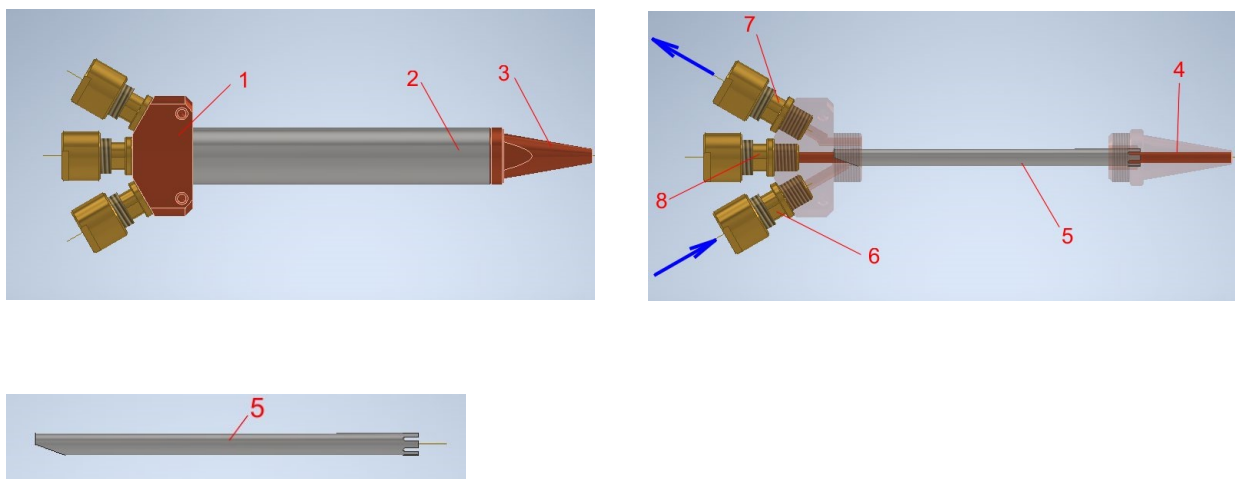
3D модель одноканального сопла для подачі газопорошкового потоку, де: : 1- основний корпус; 2- циліндрична труба; 3- сопло; 4- циліндрична труба для подачі газопорошкового потоку; 5- циліндрична труба для підведення теплоносія; 6,7,8 - штуцери для каналів підведення води та підведення газопорошкового потоку.
